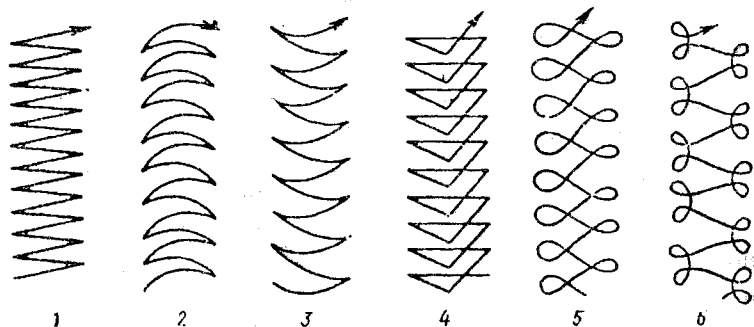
Колебательные движения концом электрода поперек шва: 1, 2, 3 — для равномерного прогрева сварочной ванны; 4 — для усиленного прогрева корня шва; 5, 6 — для усиленного прогрева кромок
